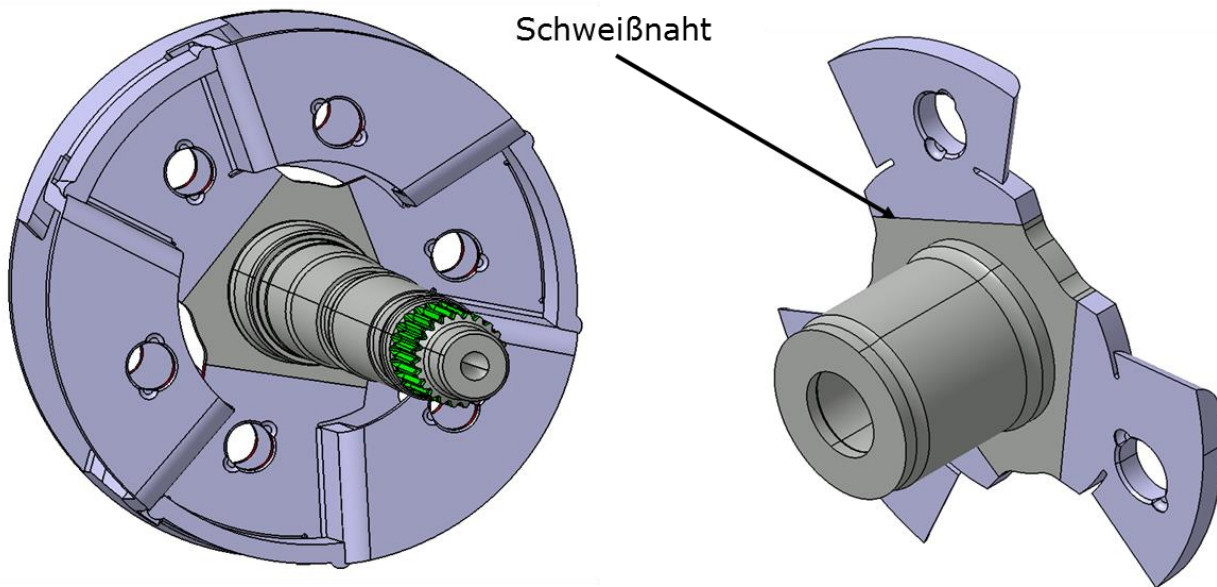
Schweißgruppe Planetenträger
